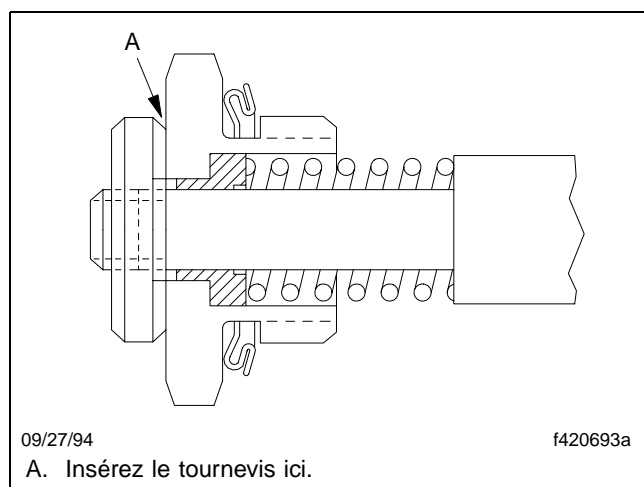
, Ensemble cliquet de rappel (vue en coupe)
